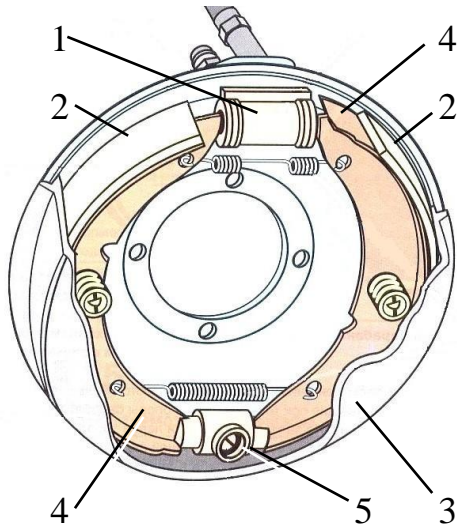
Барабанный тормозной механизм с плавающими колодками: 1 – разжимное устройство; 2 – накладки тормозных колодок; 3 – тормозной барабан; 4 – тормозные колодки; 5 – опора колодок
